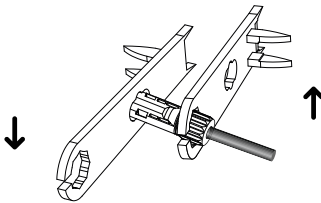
Fixieren des Kabels mit der Kabelverschraubung
